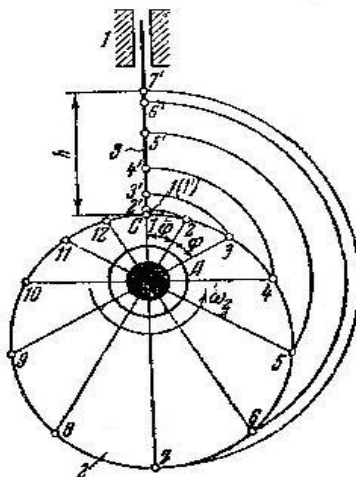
Схема кулачкового механізму зі штовхачем:
